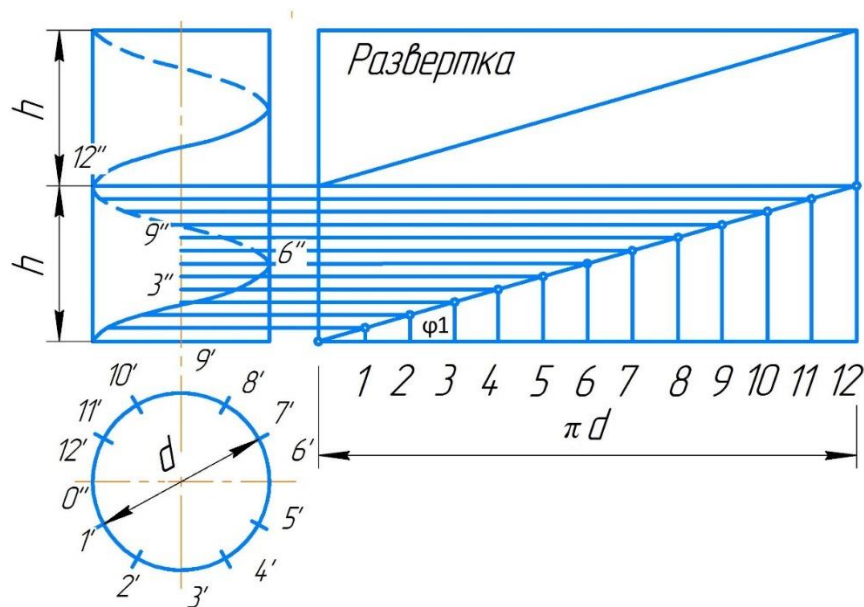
Развертка витка цилиндрической поверхности линии
